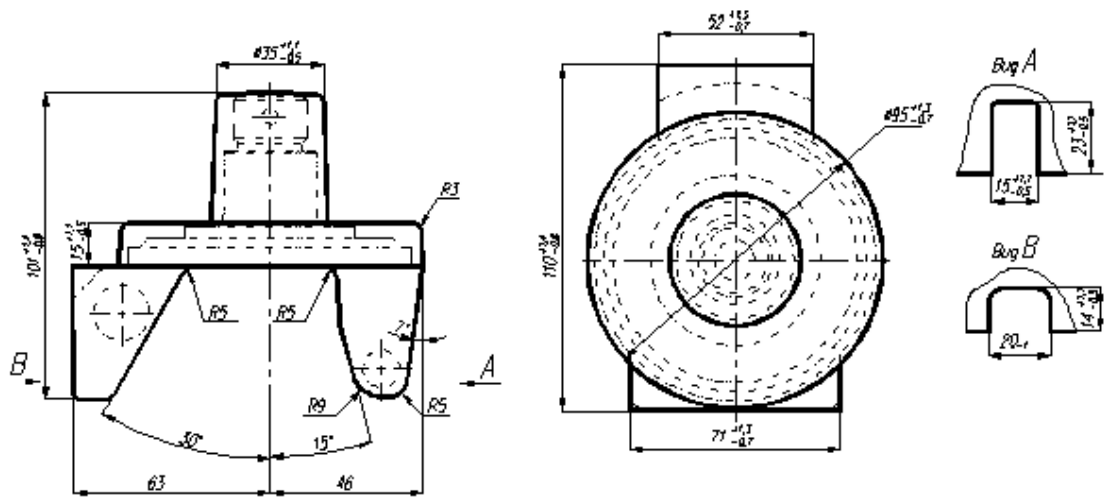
Ескіз заготовки деталі «Піввісь ПТК2211.420»
